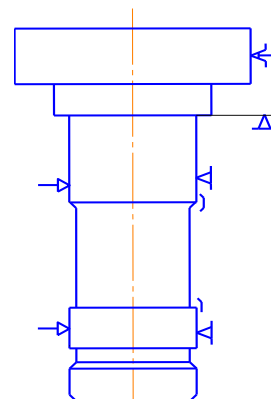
Умовна схема базування на фрезерну операцію
